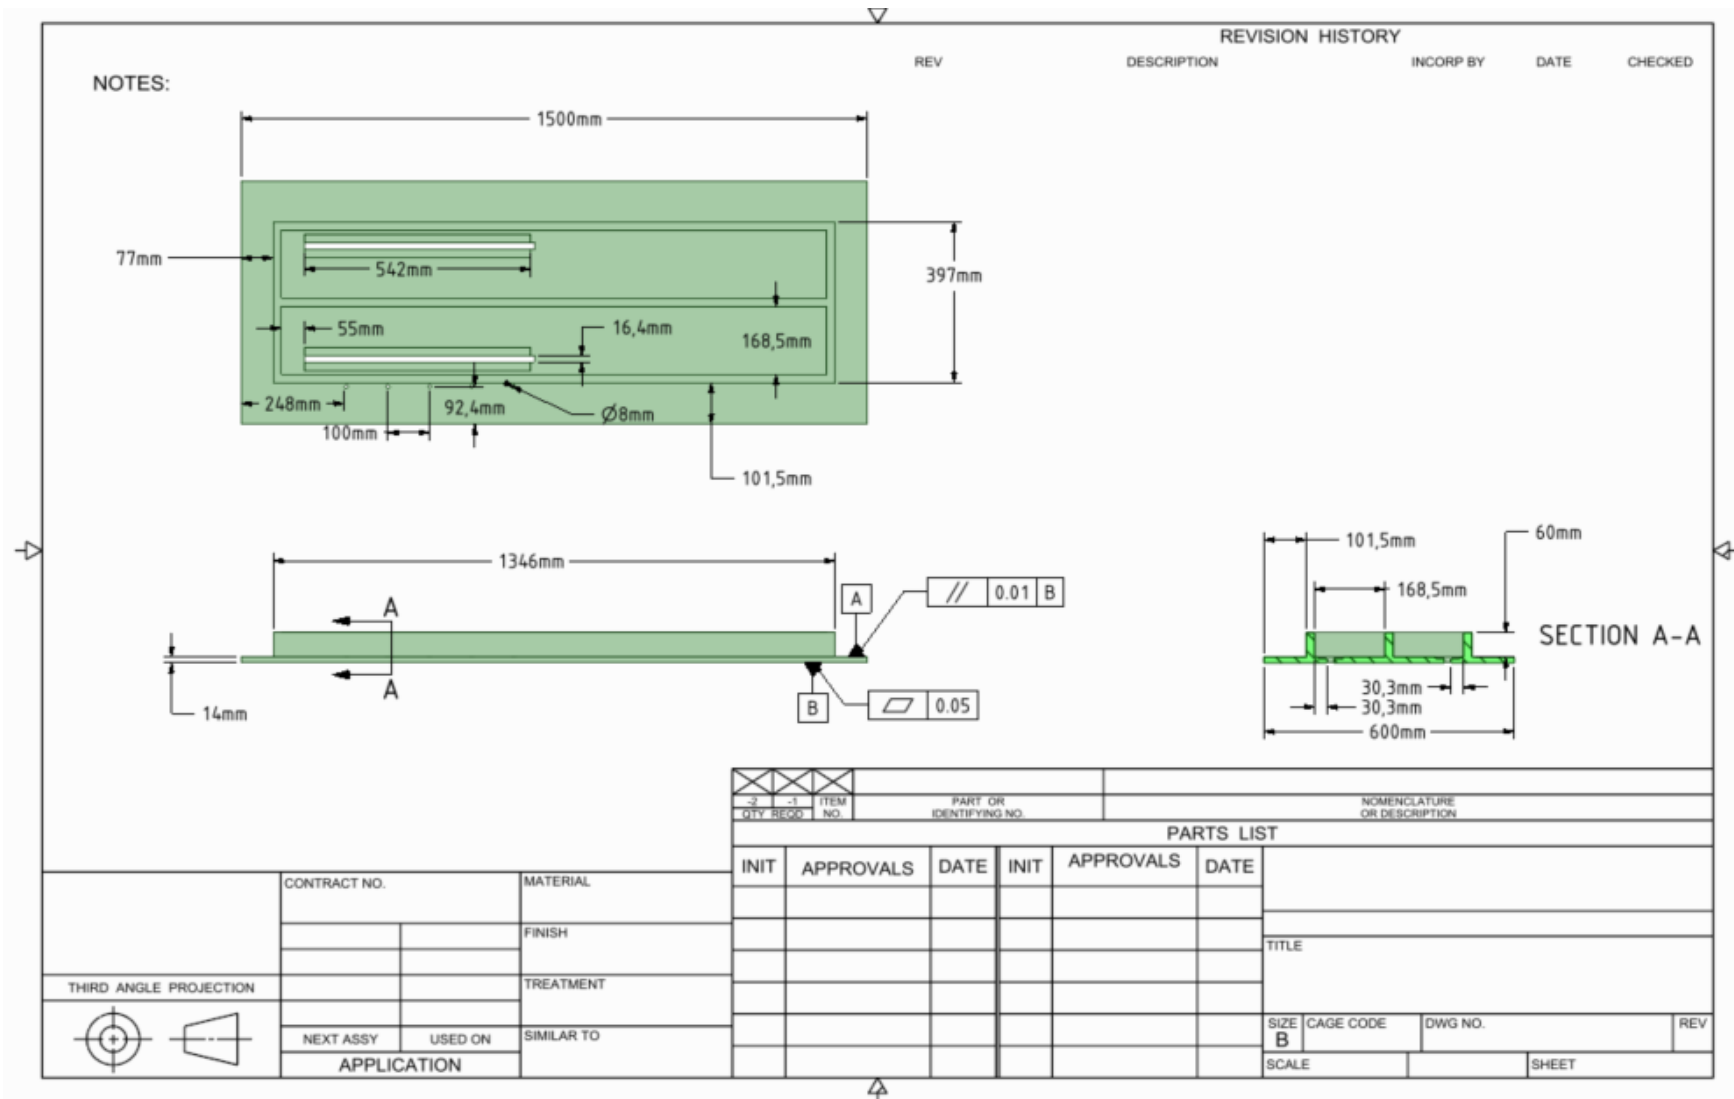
Planos de fabricación plancha superior de la bancada. Fuente: Elaboración propia.
